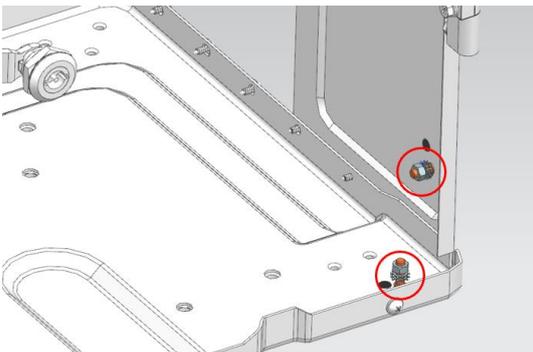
Raccordement à la terre sur le panneau de droite et sur la plateforme
